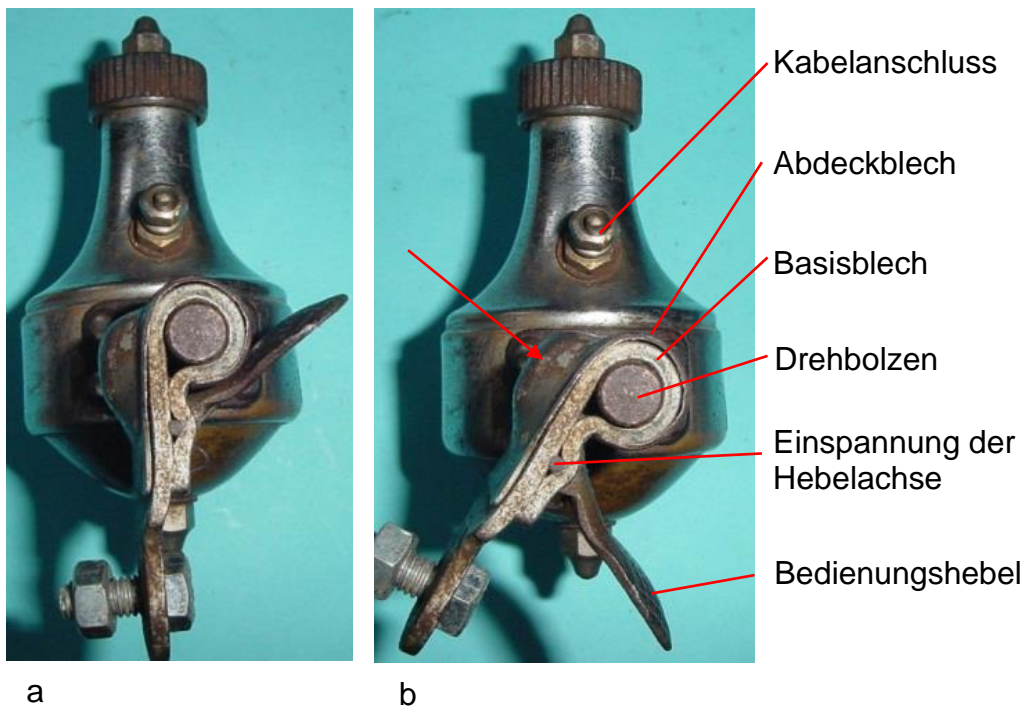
Kippvorrichtung mit den zwei ausgeprägten Positionen: a) Ruhestellung, b) Betriebsstellung
